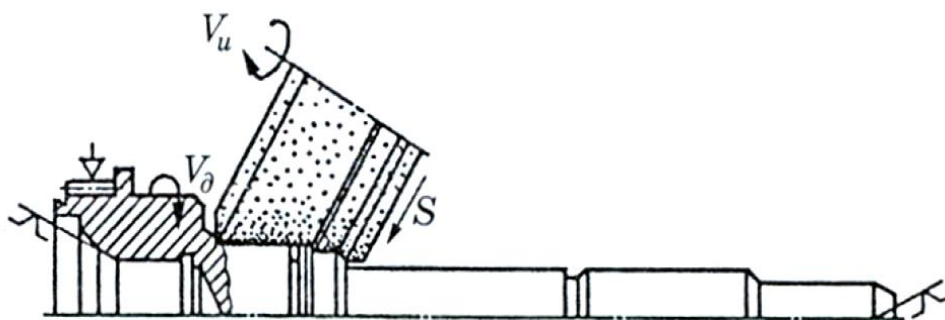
Схема одновременного шлифования пяти поверхностей детали шлифовальным кругом
